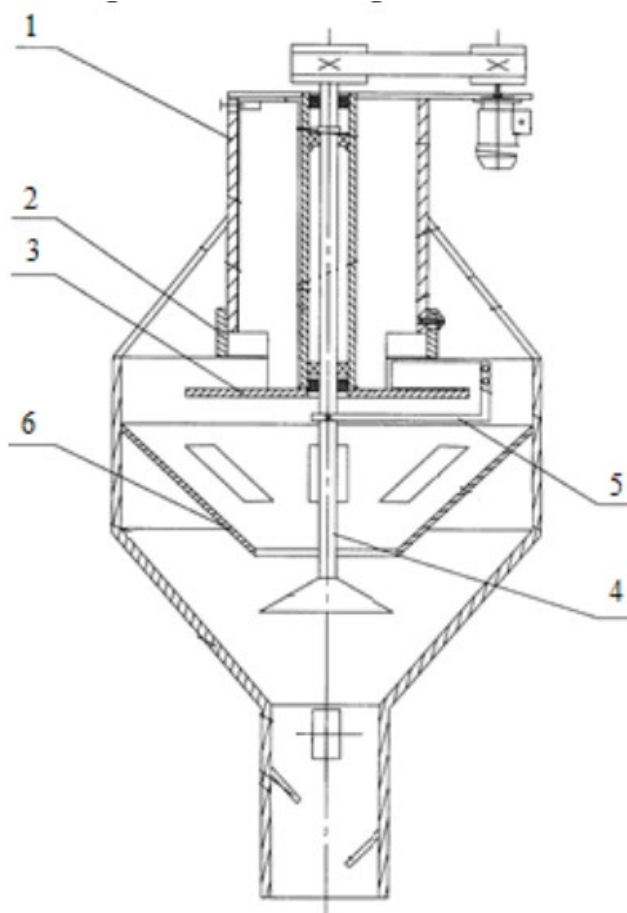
Конструктивна схема дозатора-змішувача відцентрового типу: 1 - бункер; 2 - циліндр телескопічний; 3 - диск; 4 – вал приводний; 5 – скребок; 6 - вирва
